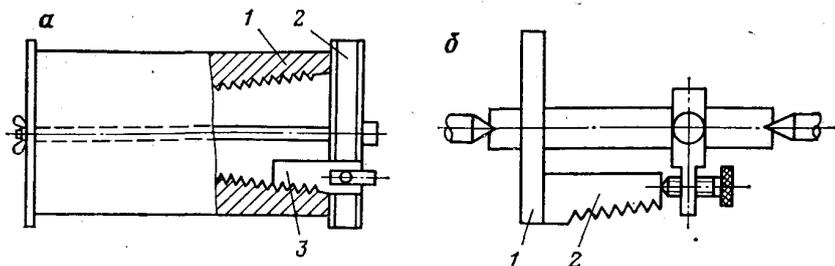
Схема проверки половины угла профиля внутренней резьбы с помощью отливки:
